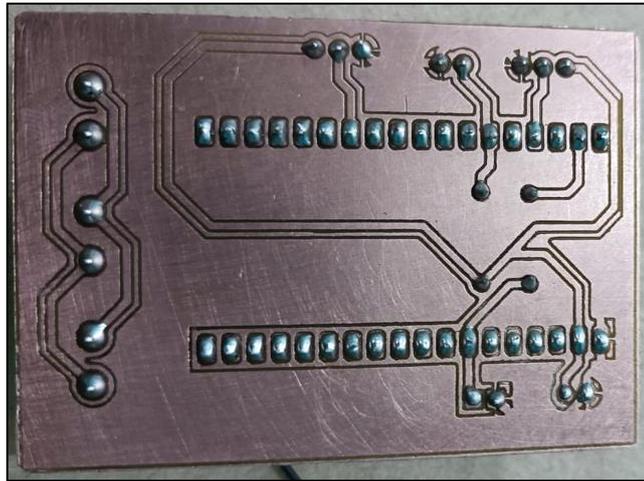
Soldadura de los dispositivos electrónicos
